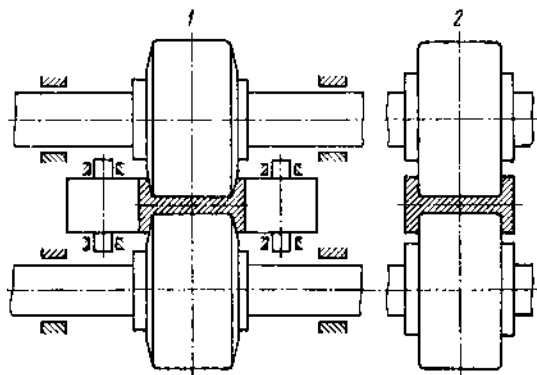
Универсальная клеть для прокатки широкополочных балок:
